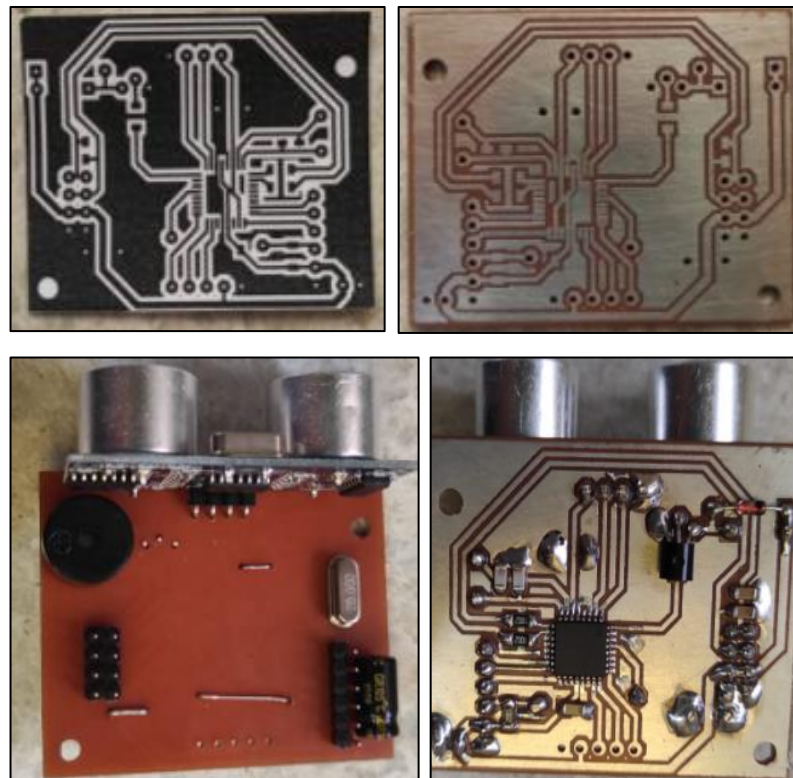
Impresión de circuito y soldadura de elementos electrónicos
